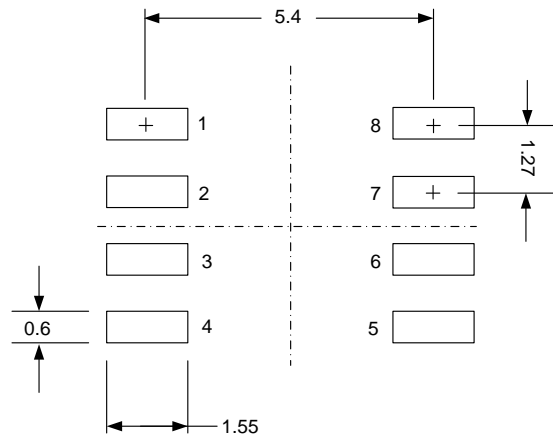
SOP-8L(150mil)焊盘细节图 (所有尺寸单位为 mm)
